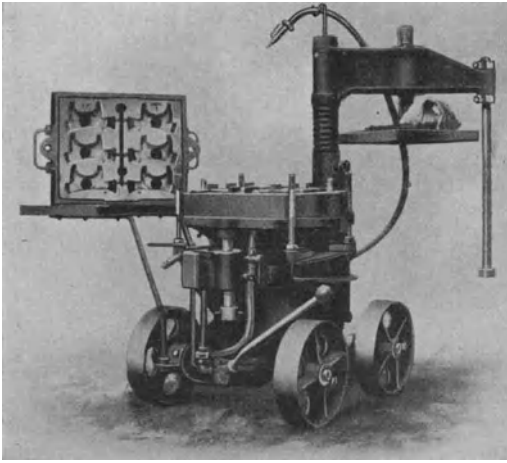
Druckluft-Rüttel- und Preßformmaschine.
